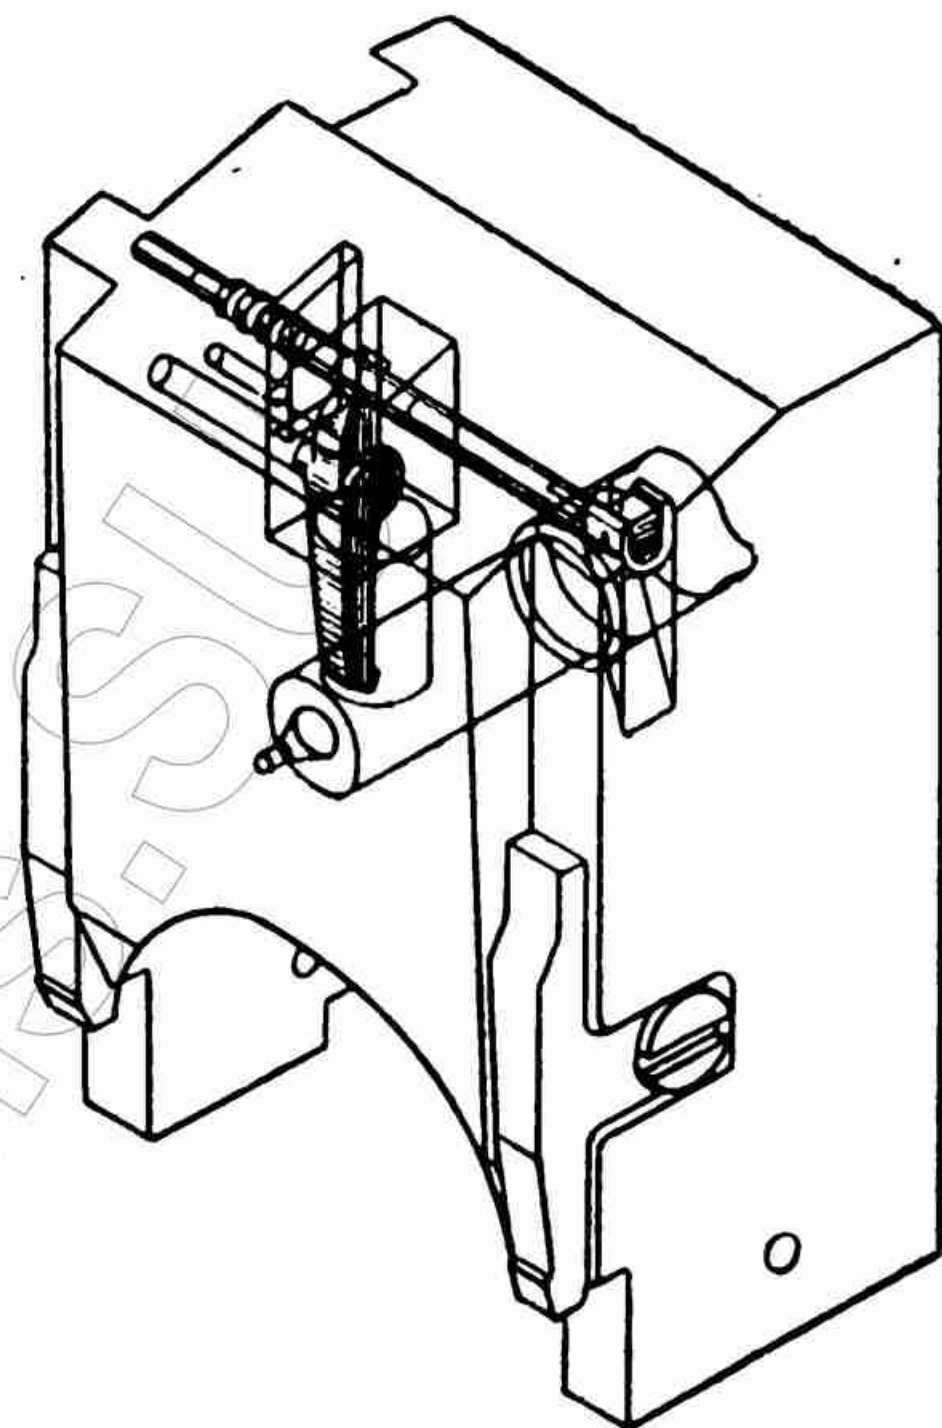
Детали ударного и предохранительного механизмов при сборке (вторая операция)
